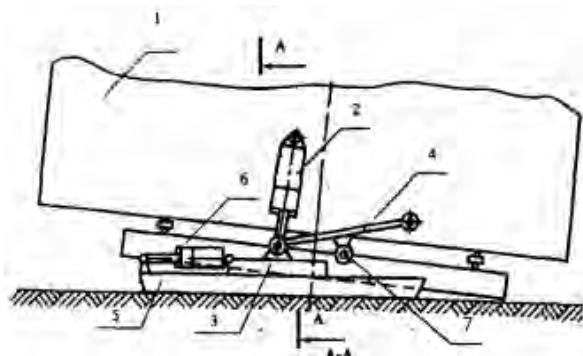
Схема трёхопорного механизма шагания с неполным отрывом базы:
